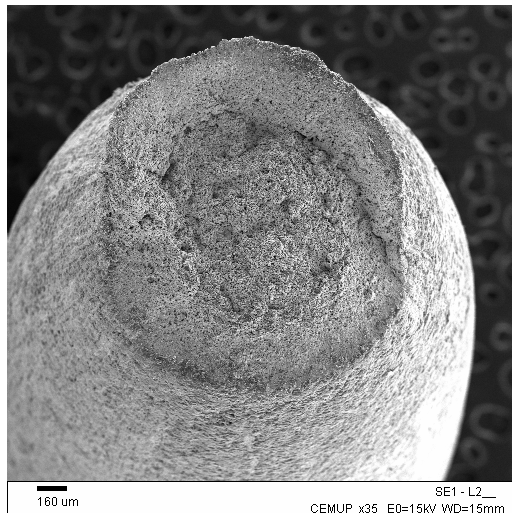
Aspecto da superfície de fractura do provete L2 (fracturado) (35X).
